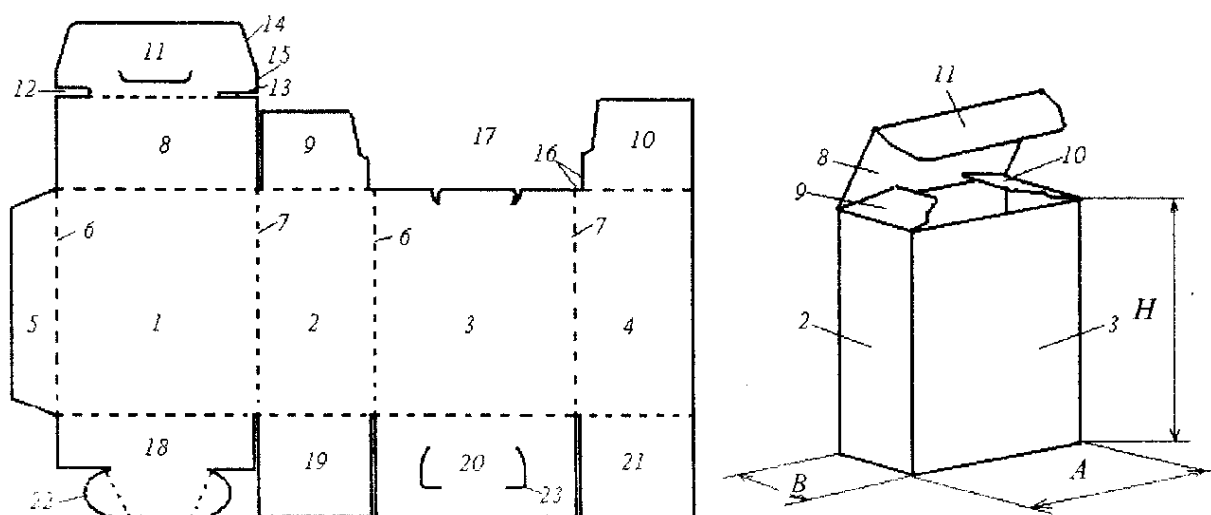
Основные элементы развертки складных коробок и собранный ящик
